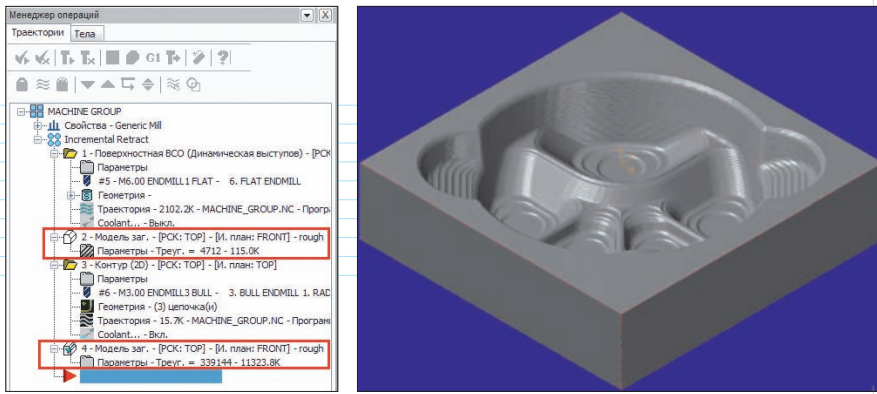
Операции “Модель заготовки” и визуализация заготовки после черновой обработки
